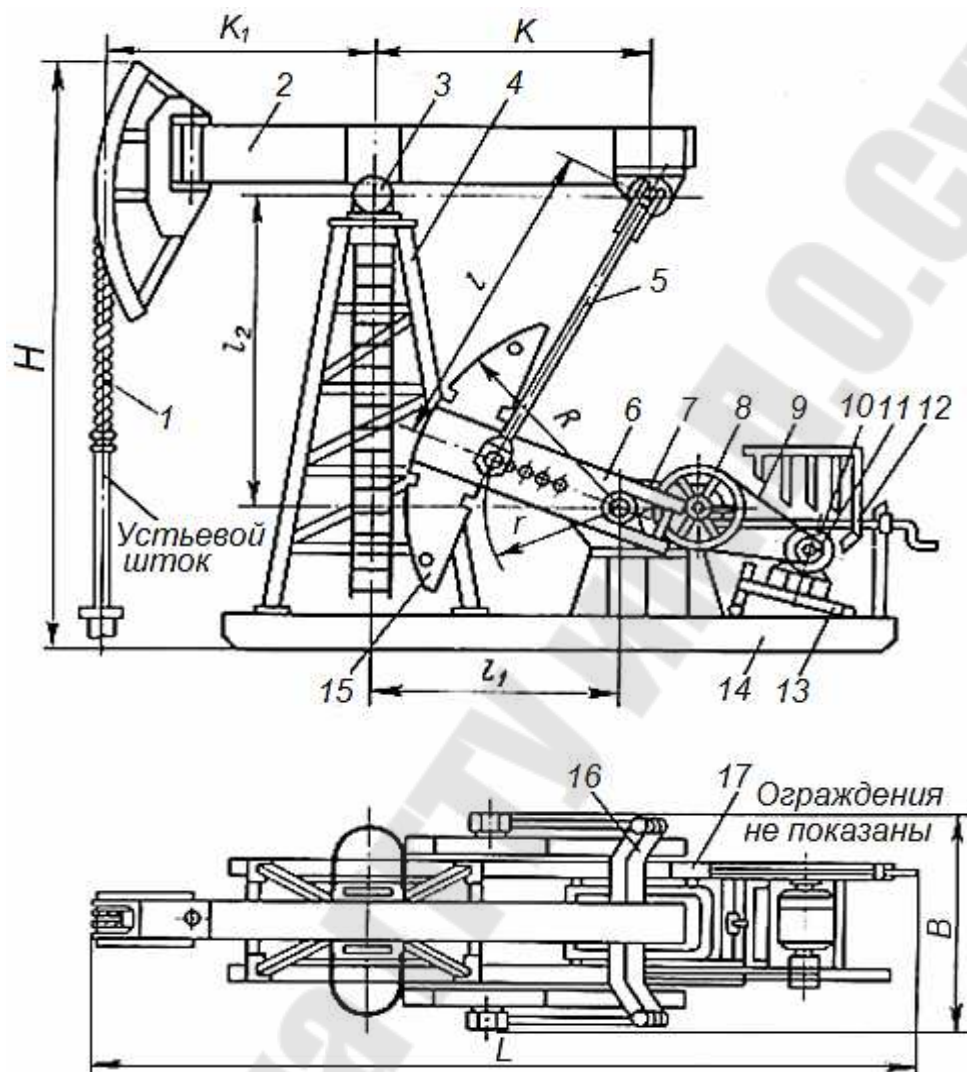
Схема балансирующего станка-качалки: 1 – канатная подвеска; 2 – балансир с поворотной головкой; 3 – опора балансира; 4 – стойка; 5 – шатун; 6 – кривошип; 7 – редуктор; 8 – ведомый шкив; 9 – клиноременная передача; 10 – электродвигатель; 11 – ведущий шкив; 12 – ограждения; 13 – салазки поворотные для электродвигателя; 14 – рама, 15 – противовес, 16 – траверса, 17 – тормозной шкив
